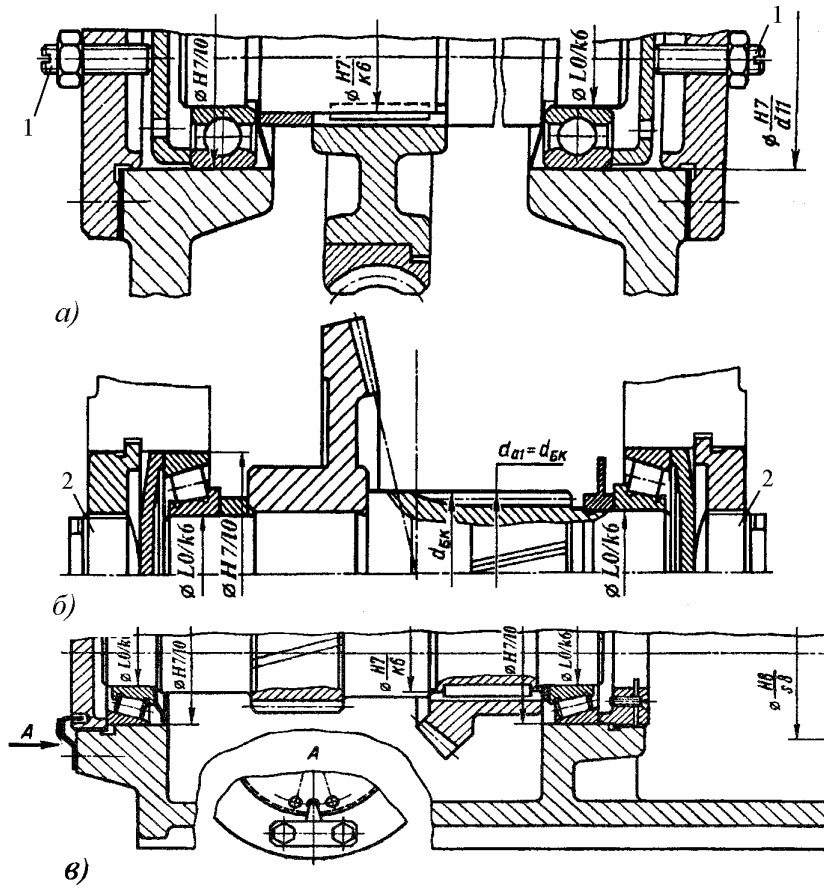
Регулирование зацепления и осевого зазора в радиально-упорных подшипниках винтами через нажимные шайбы и резьбовыми крышками
